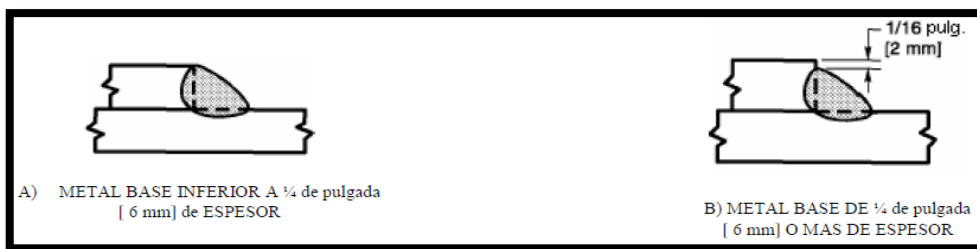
Tamaño máximo de soldadura de filete en los bordes de las uniones traslapadas
